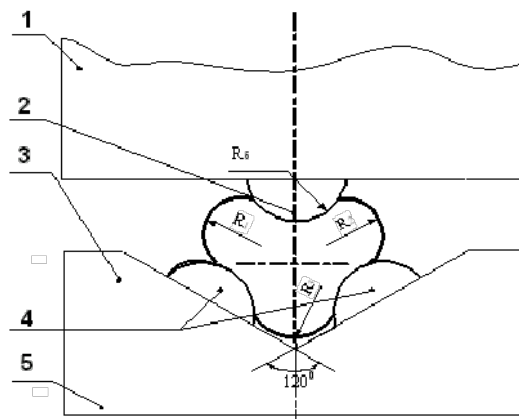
Обжатие заготовки комбинированными профилированными бойками
